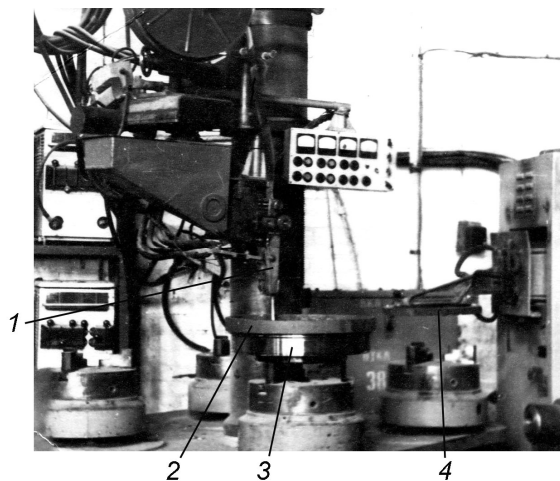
Четырехпозиционная установка для наплавки горизонтальных поверхностей тел вращения: 1 – приставка для подачи ленточного электрода с одновременным его профилированием; 2 – медный кокиль; 3 – наплавляемая деталь; 4 – индуктор ТВЧ
